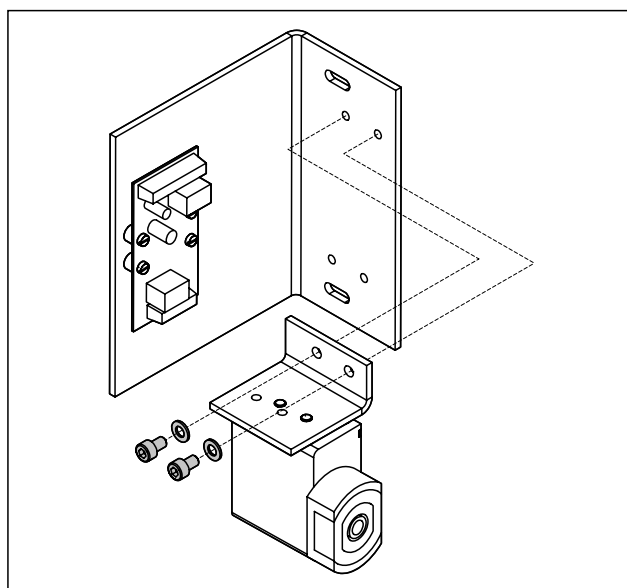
Den Haftmagnet an den Montagewinkel schrauben
